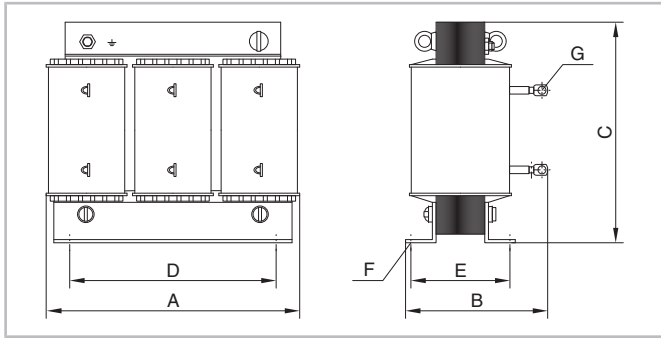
Габаритные чертежи линейных реакторов 182-KC.. 330-KC
